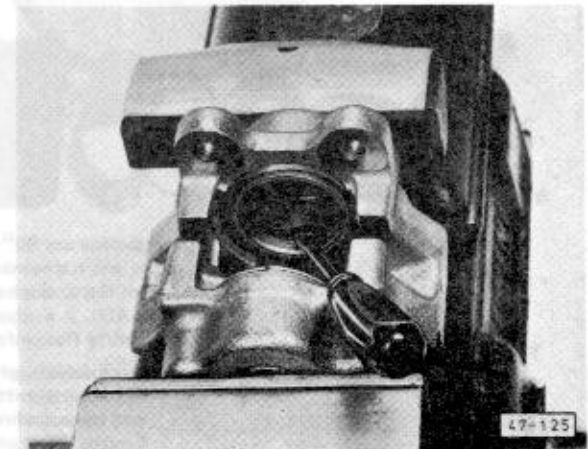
Dichtring vorsichtig mit einem Schraubenzieher ausbauen
